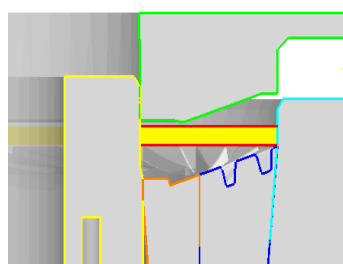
Схема процесса: 1. Заготовка; 2. Пуансон; 3. Центральная вставка; 4. Формовочная матрица; 5. Формовочная матрица; 6. Внешняя вставка.
